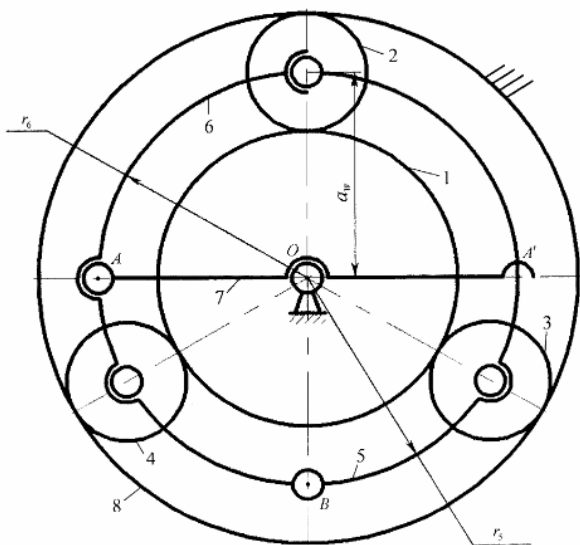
Схематическое изображение трехсателлитного планетарного механизма, предложенного Хайдуковой Я.А. [3]
